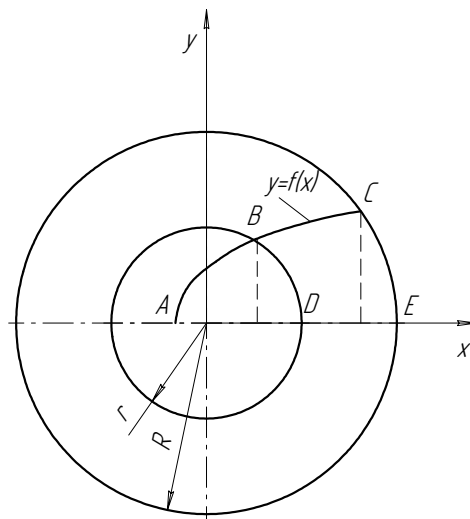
До визначення площі контакту інструменту із заготовкою із врахуванням утворення пластичної хвилі
